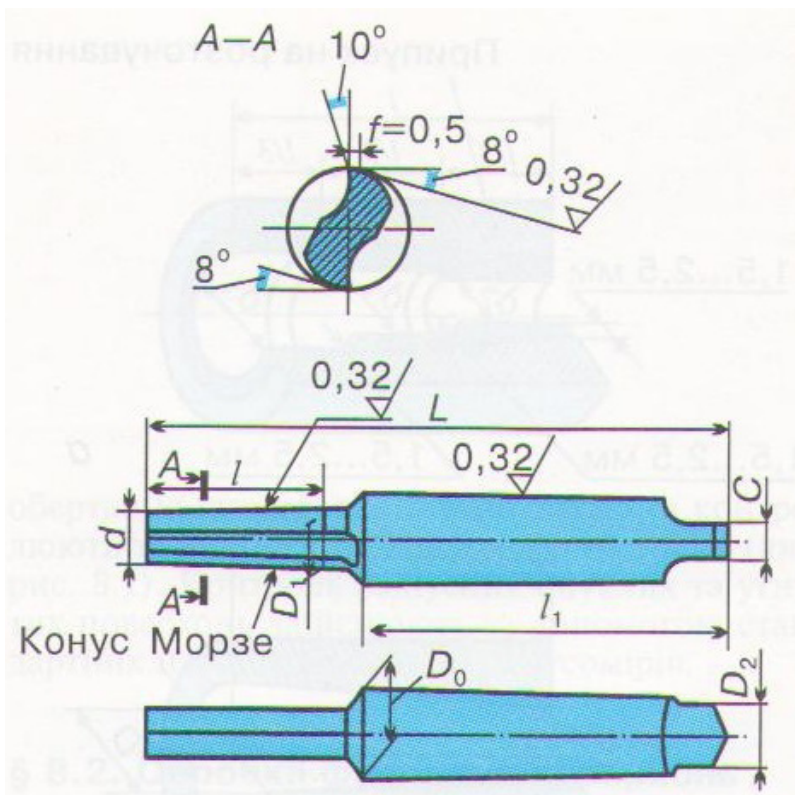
Двоперовий конічний зенкер (ніж) для обробки стандартних конусів Морзе
